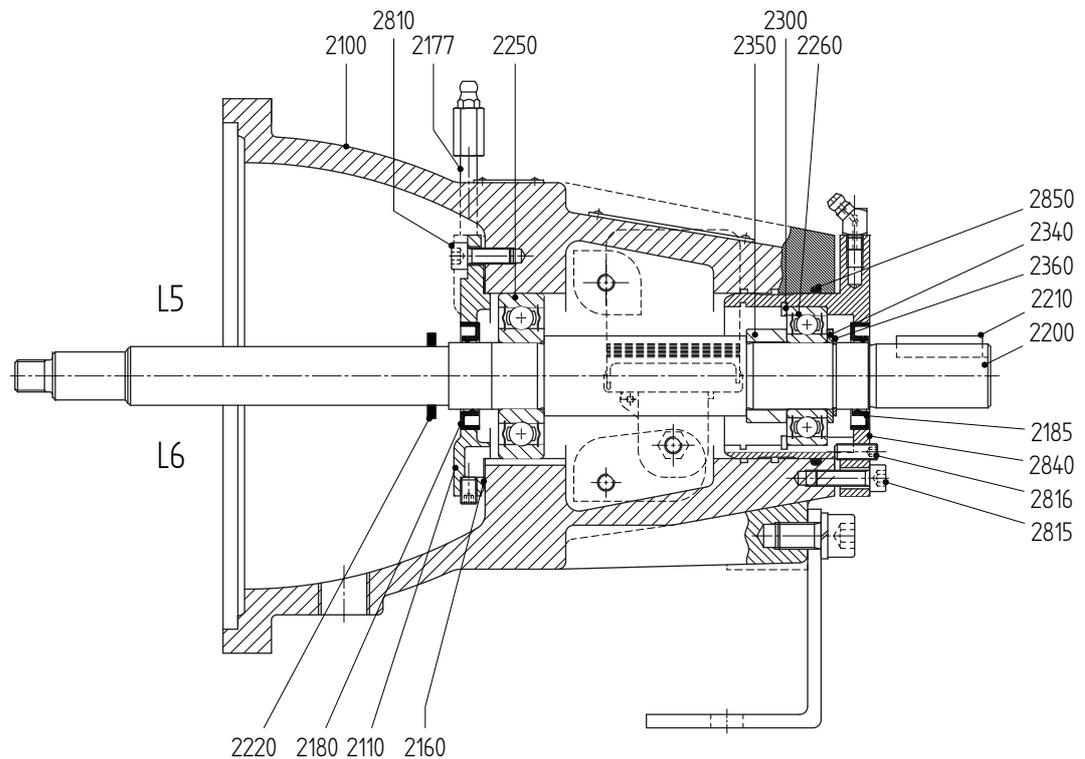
Подшипник L5, L6 типов 25-125, 25-160
